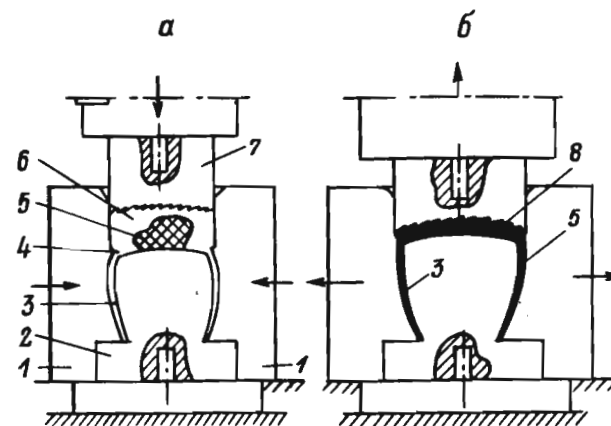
Схема формирования галош методом штампования: а — опускание плунжера; б — подъем плунжера и размыкание формы; 1 — матрица; 2 — сердечник; 3 — текстильный каркас; 4 — кольцевой зазор; 5 — резиновая смесь (заготовка); 6 — камера; 7 — плунжер-пуансон; 8 — отформованная галоша
